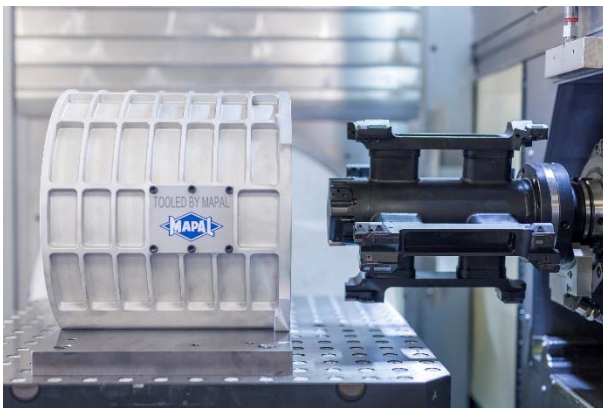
Mit einem Feinbohrwerkzeug als Schweißkonstruktion wird die Hauptbohrung des Zentralgehäuses auf wenige  $\mu\text{m}$  genau bearbeitet.
